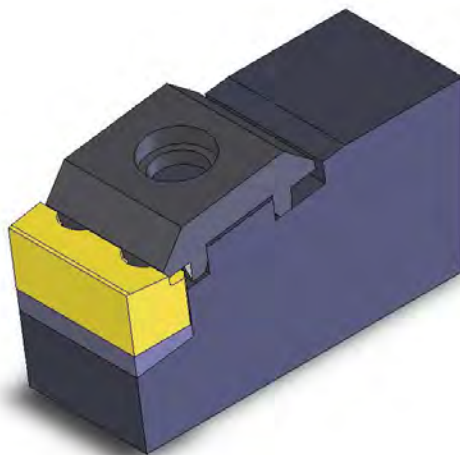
Прогресивна конструкція вузла кріплення різальної пластини збірного прорізного токарного різця для важкого різання
